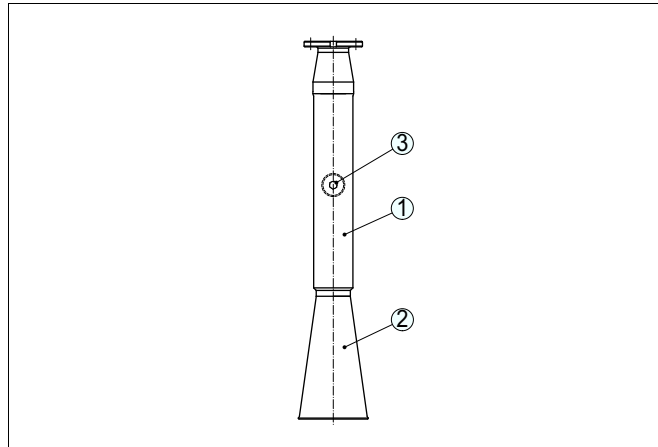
Prolongación uniseccional recta, con antena de trompeta soldada
